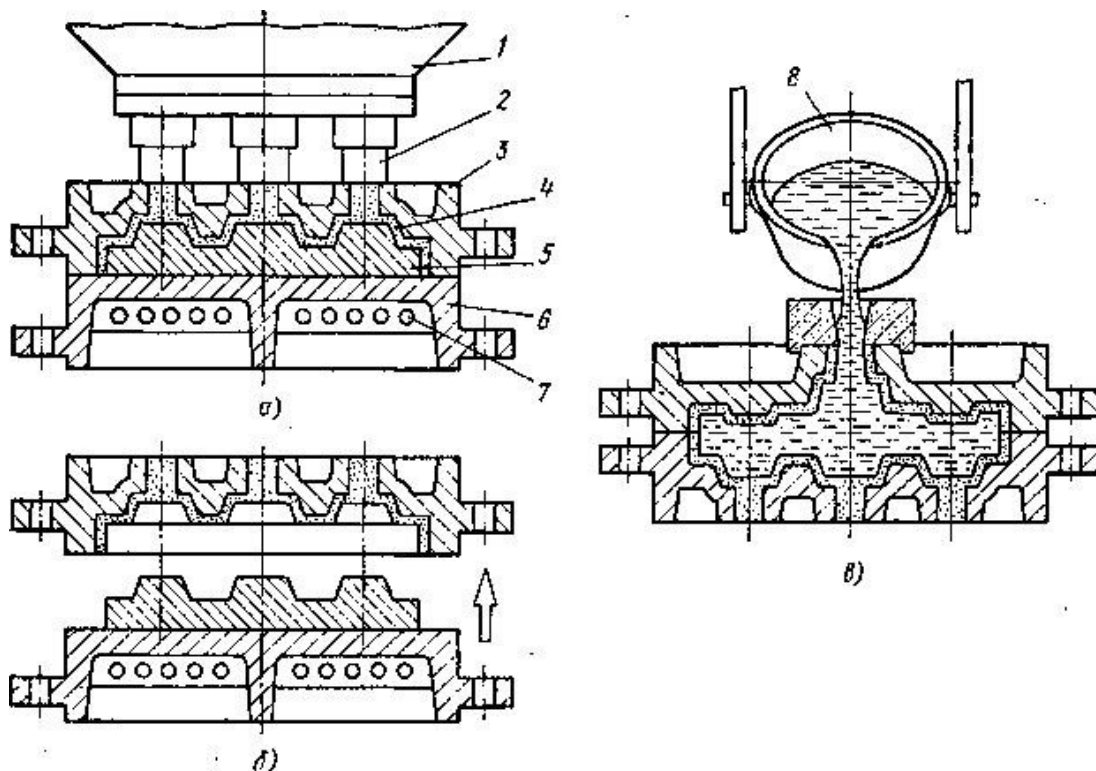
Схема процесса изготовления отливок в облицованные кокили
